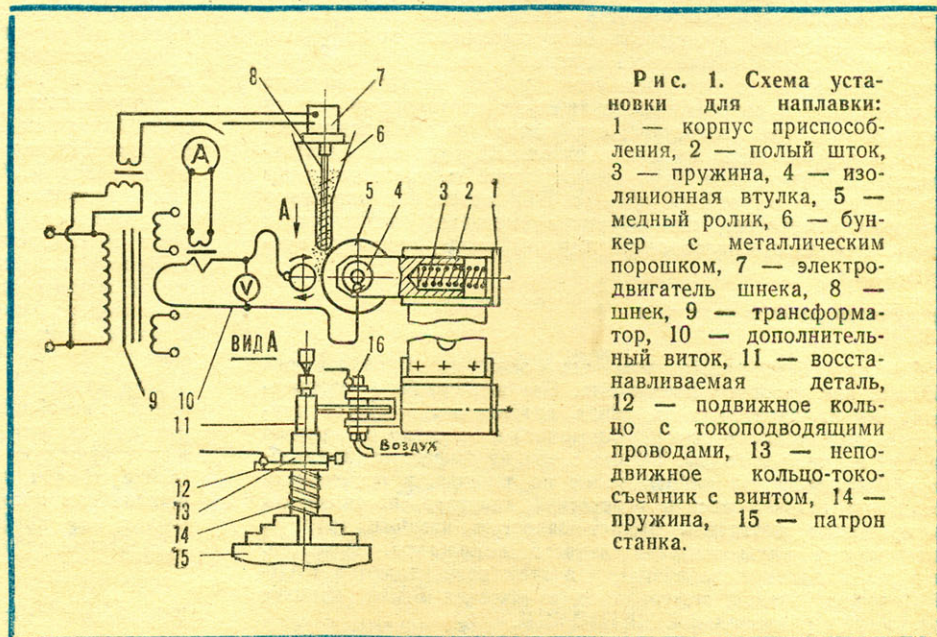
Схема установки для наплавки: 1 — корпус приспособления, 2 — полый шток, 3 — пружина, 4 — изоляционная втулка, 5 — медный ролик, 6 — бункер с металлическим порошком, 7 — электродвигатель шнека, 8 — шнек, 9 — трансформатор, 10 — дополнительный виток, 11 — восстанавливаемая деталь, 12 — подвижное кольцо с токоподводящими проводами, 13 — неподвижное кольцо-токосъемник с винтом, 14 — пружина, 15 — патрон станка.
